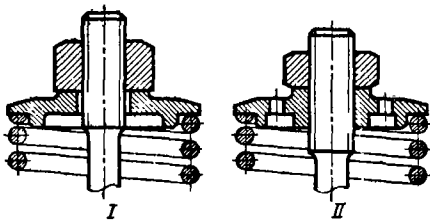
Затяжка пружины. Стопорение гаек: I — силой упругости пружины; II — контргайкой
